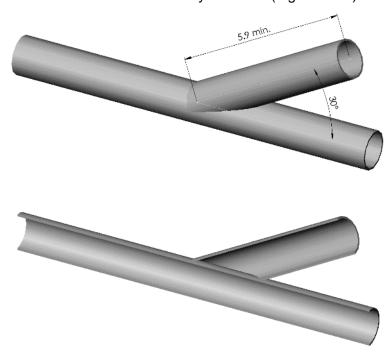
Jaula Antivuelco, Muestra de soldadura 2
